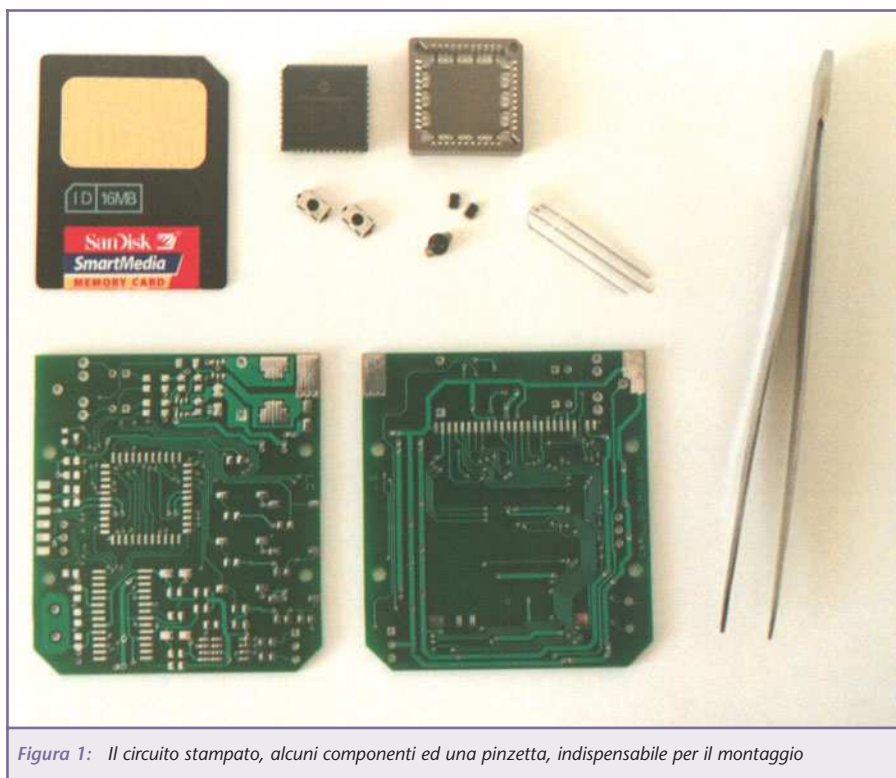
Il circuito stampato, alcuni componenti ed una pinzetta, indispensabile per il montaggio
